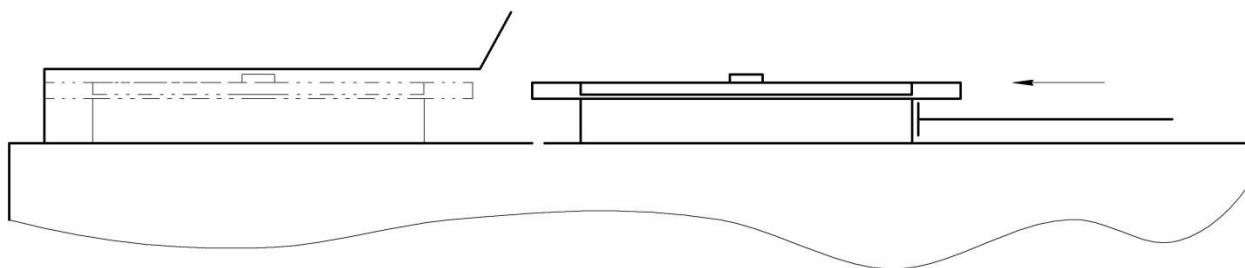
Схема позиции III четырехпозиционного роторного сборочного автомата 9
